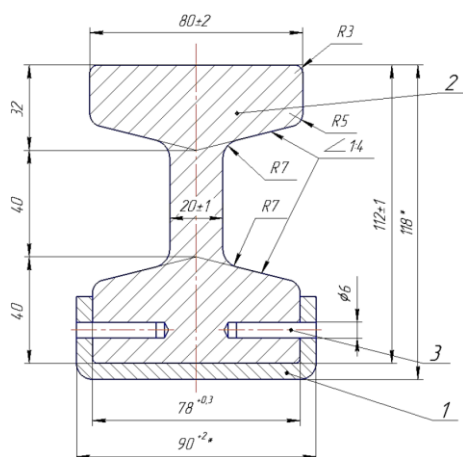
Конструкция и размеры сечения рельса РСК 118
